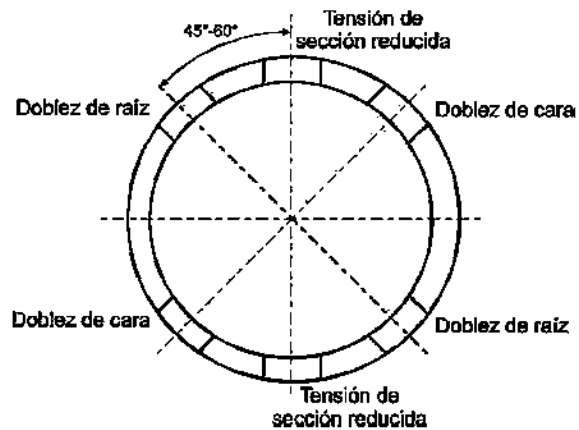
Seccionamiento de las uniones soldadas disímiles.
